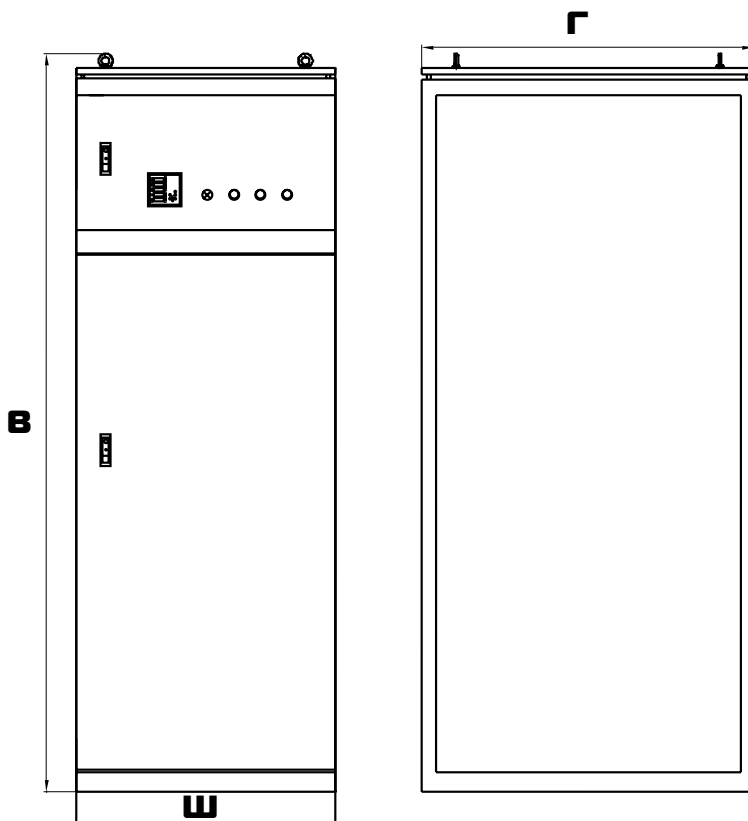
Габаритный чертеж трехфазного СТЭМ-2 IP20 630 кВА
